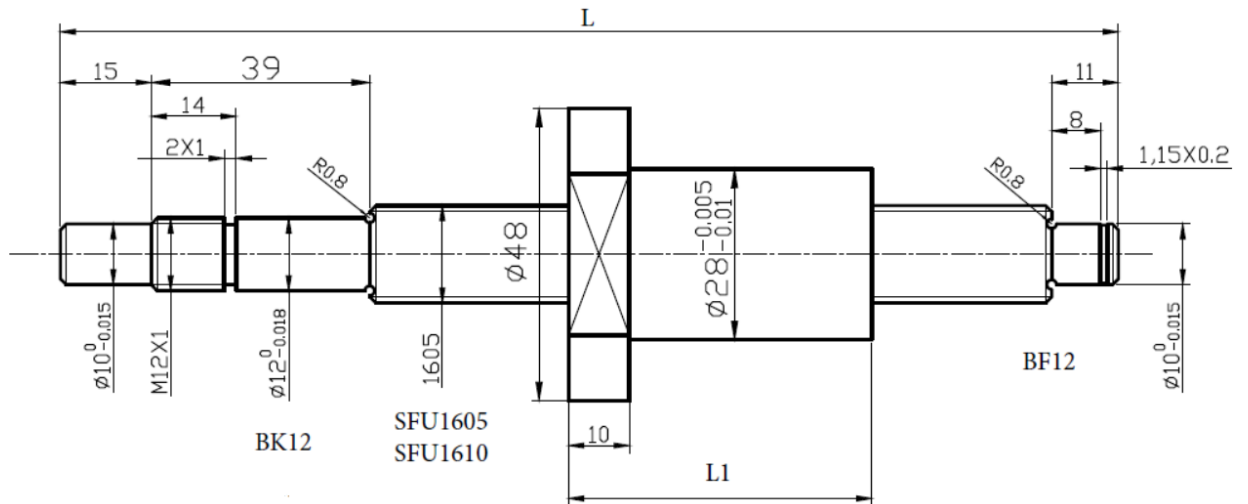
Dimensiones de tornillo de bola, unidades en milímetros.
